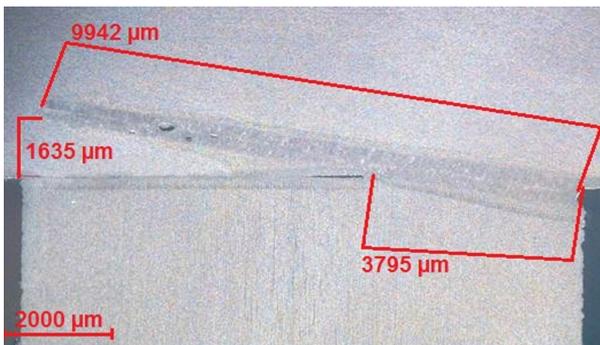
Schliffbild eines T-Stoßes, Materialdicke $t = 10$ mm, $P_L = 18$ kW (Quelle: iLAS / Carl Cloos Schweißtechnik)
